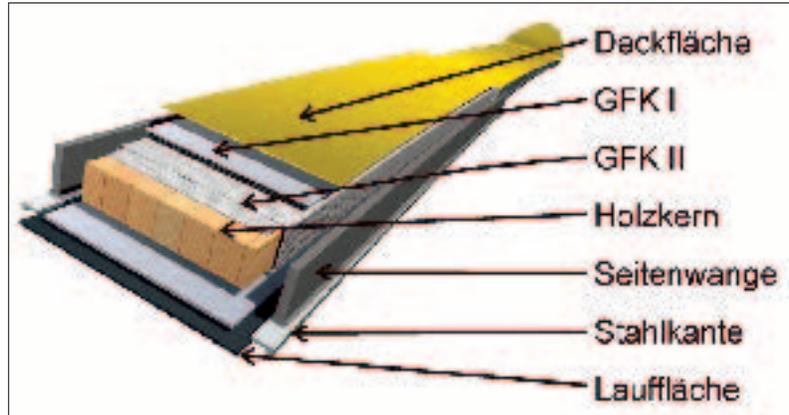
Aufbau des untersuchten Skimodells [Bild Völkl GmbH & Co. KG]. Investigated ski design [courtesy of Völkl GmbH & Co. KG].
